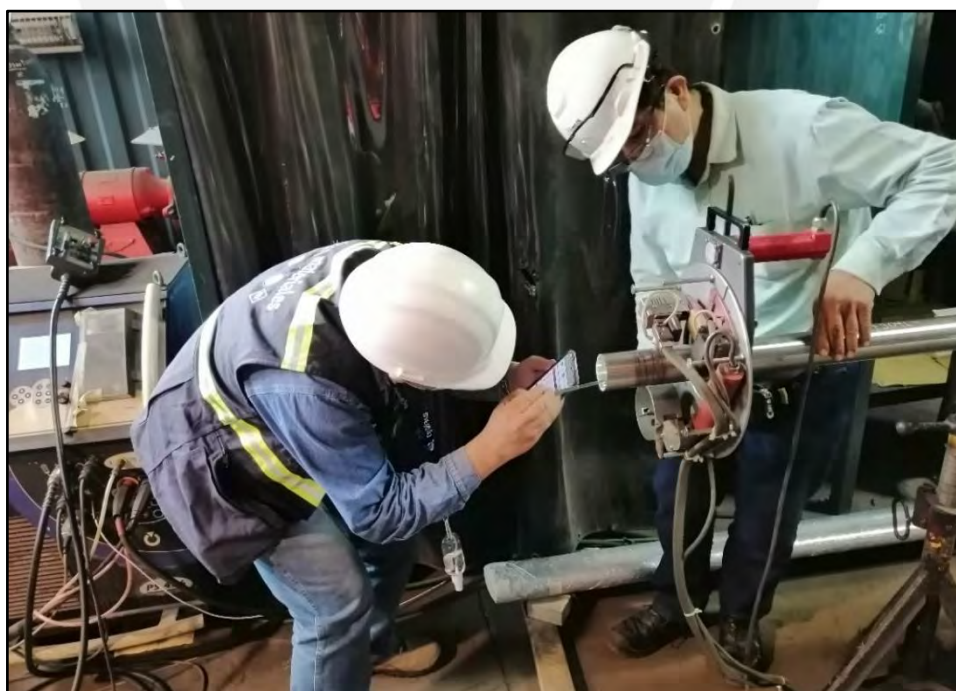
Inspección visual en la raíz de la zona de fusión ejecutada con los parámetros de soldadura de la Tabla 16.
